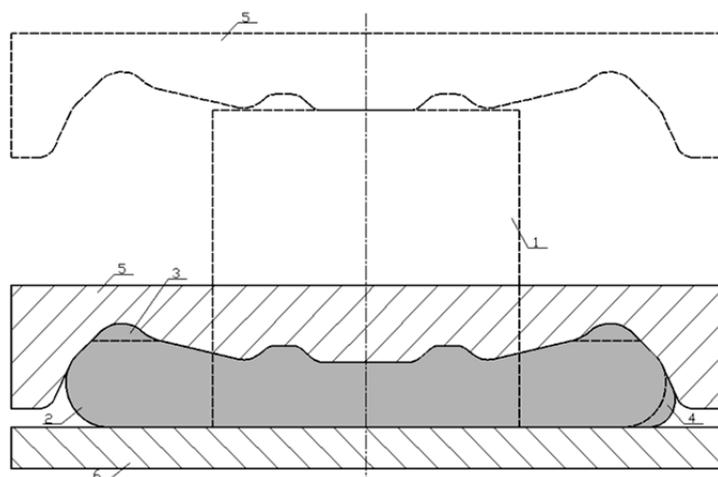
Схема осадки и совмещенной с ней разгонки заготовки (рассмотрен вариант получения асимметричной заготовки):
